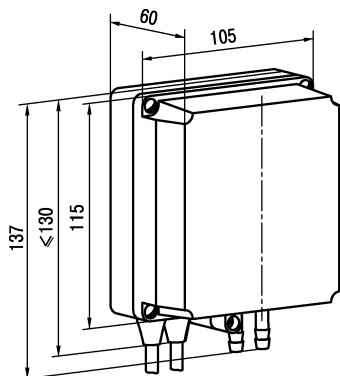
Габаритные размеры преобразователь настенного крепления
